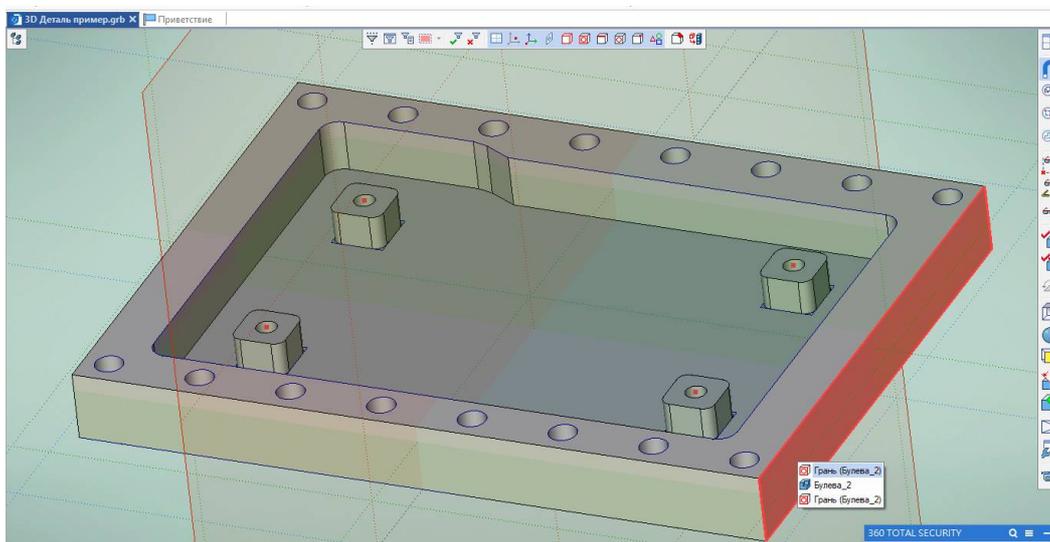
3D-модель детали в T-Flex CAD3D
